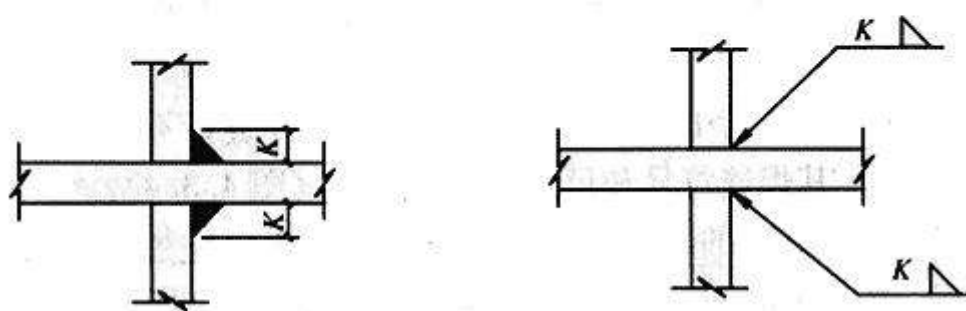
3个及以上焊件的焊缝标注方法
